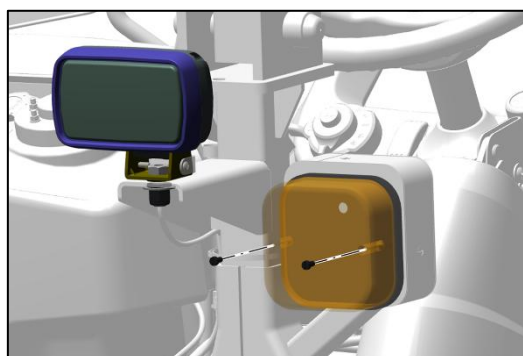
REMPLACEMENT DE L'AMPOULE D'UN CLIGNOTANT ARRIÈRE
